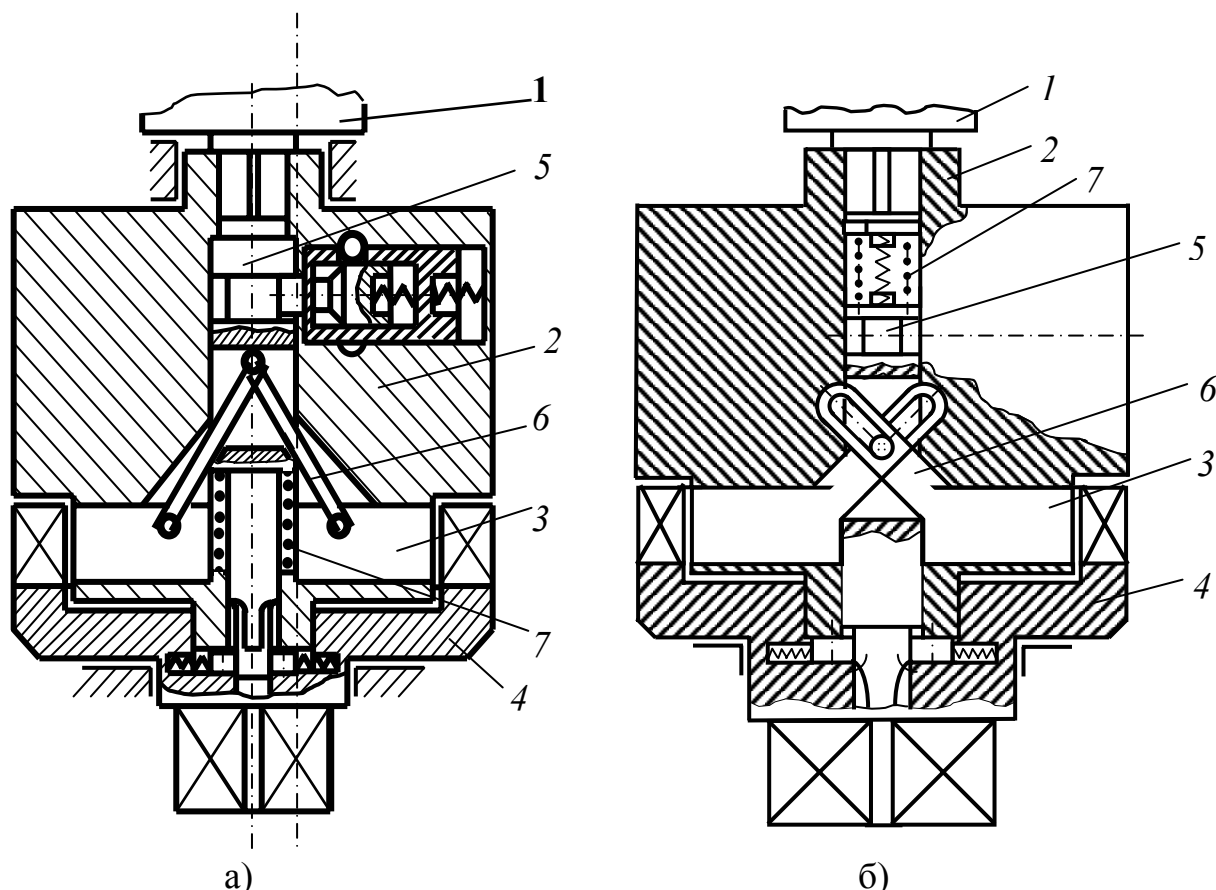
Принципиальные схемы редкоударных механизмов резьбозавертывающего инструмента с радиально перемещающимися бойками:
